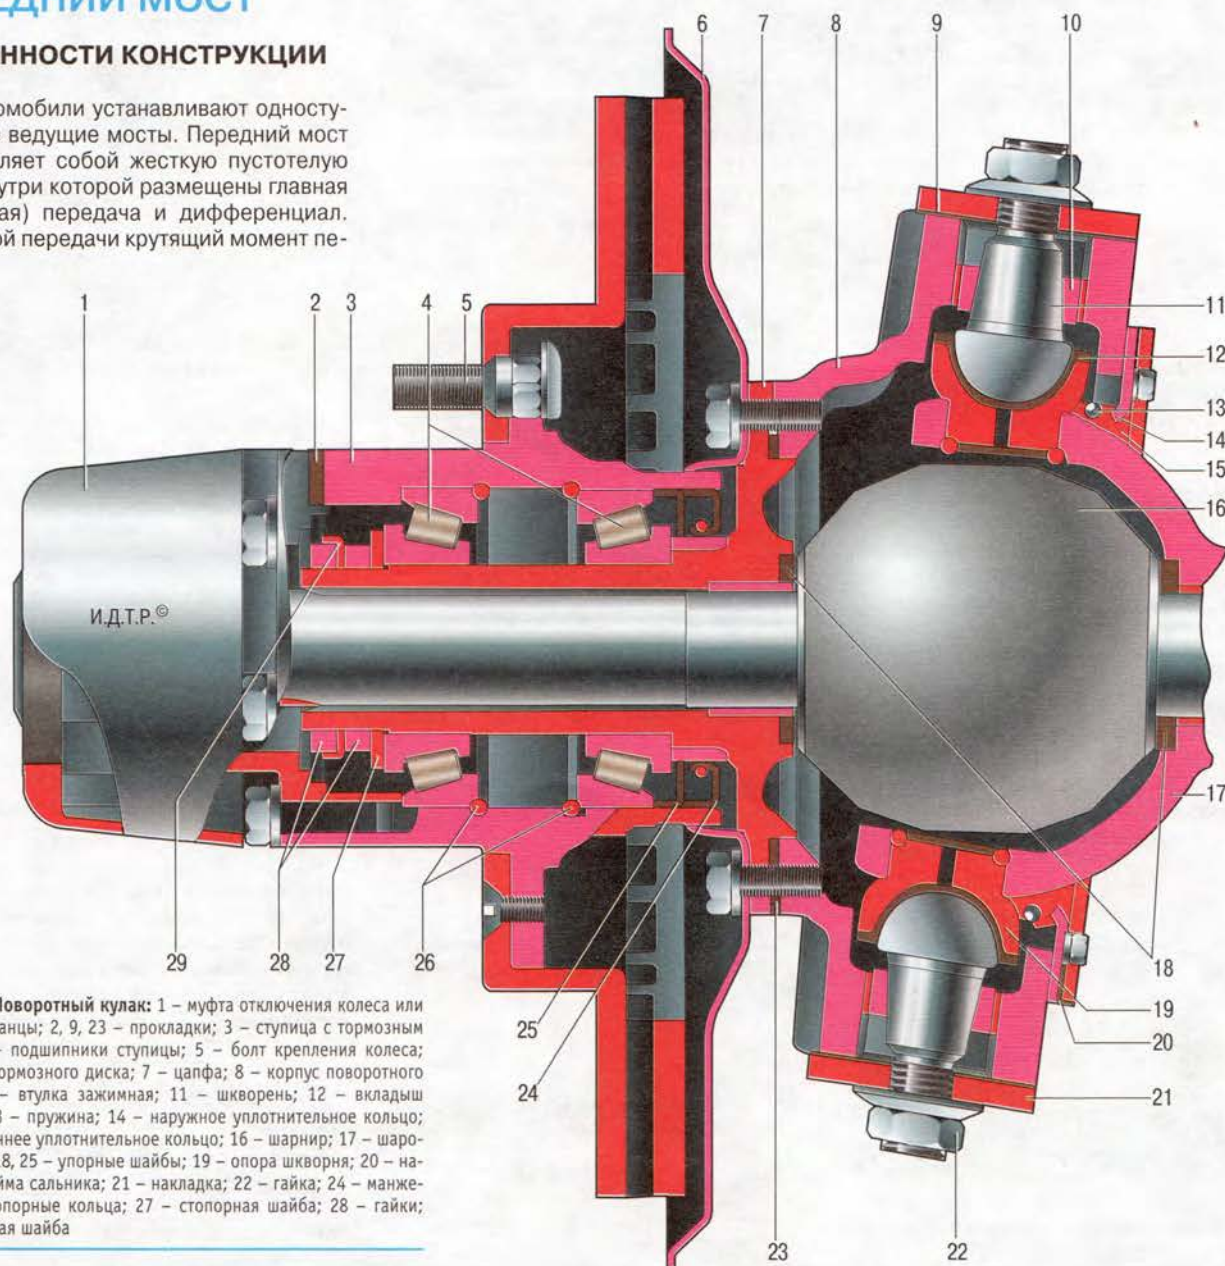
Поворотный кулак: 1 – муфта отключения колеса или ведущие фланцы; 2, 9, 23 – прокладки; 3 – ступица с тормозным диском; 4 – подшипники ступицы; 5 – болт крепления колеса; 6 – щиток тормозного диска; 7 – цапфа; 8 – корпус поворотного кулака; 10 – втулка зажимная; 11 – шкворень; 12 – вкладыш шкворня; 13 – пружина; 14 – наружное уплотнительное кольцо; 15 – внутреннее уплотнительное кольцо; 16 – шарнир; 17 – шаровая опора; 18, 25 – упорные шайбы; 19 – опора шкворня; 20 – наружная обойма сальника; 21 – накладка; 22 – гайка; 24 – манжета; 26 – стопорные кольца; 27 – стопорная шайба; 28 – гайки; 29 – замочная шайба
